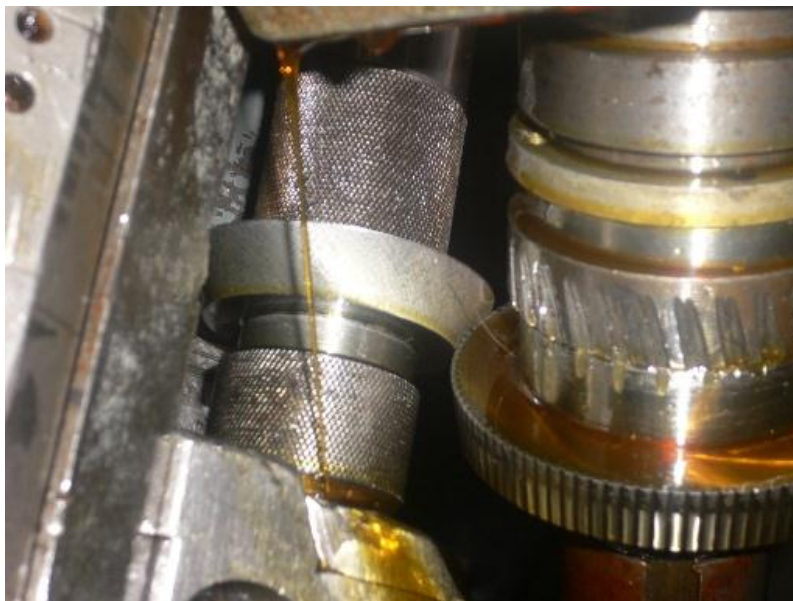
Фото процесу виготовлення гіперболоїдної заготовки
